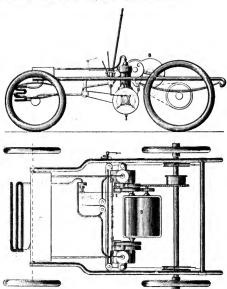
u. 6, Aufriss and Grundriss des Wagens Legrand.
